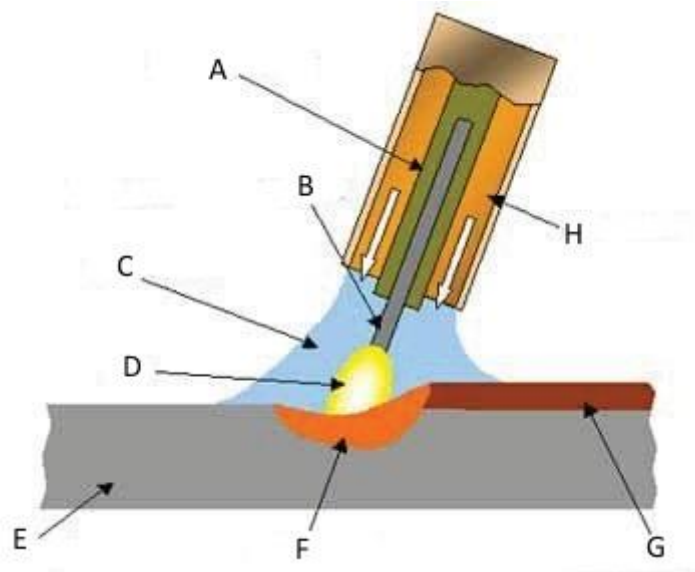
O processo de soldadura MAG. A. Tubo de contato, B. Eléctrodo consumível, C. Proteção contra gás, D. Arco, E. Peça de trabalho, F. Banho de solda, G. Metal de solda, H. Bocal de gás. Fonte: TWI
